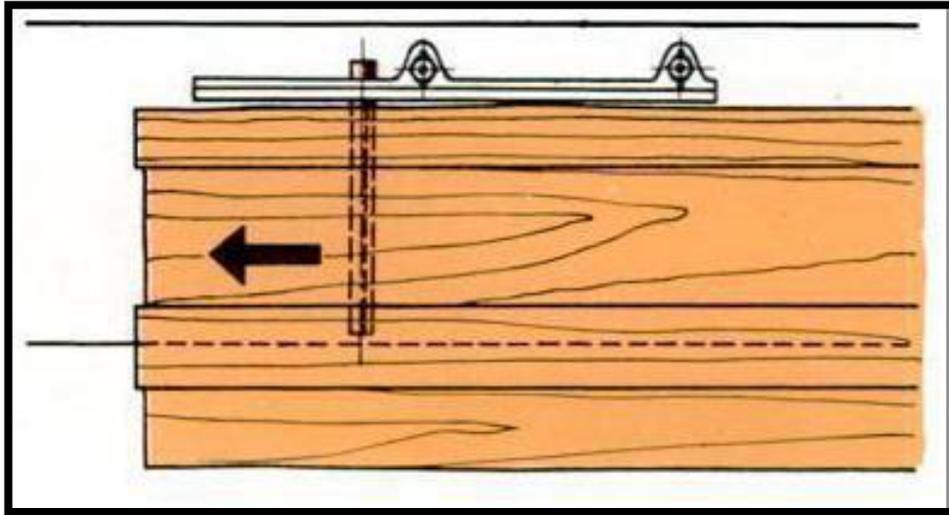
PARA TABLAS CORTAS SE RECURRE AL AUXILIO DE UNA PIEZA AUXILIAR DE CONDUCCIÓN
